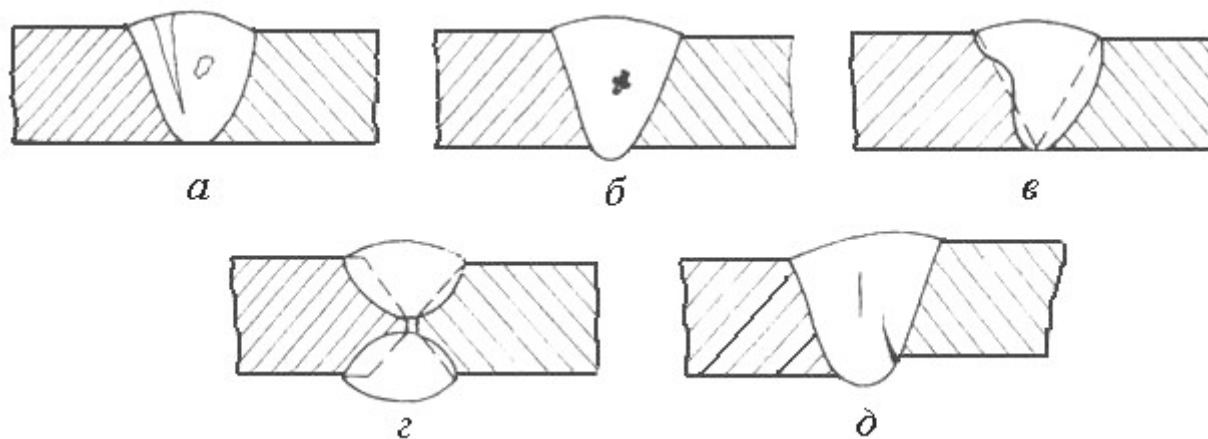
Виды внутренних дефектов сварных соединений: *a* – поры и свищи; *б* – твердые включения (шлак); *в* – несплавление; *г* – непровар; *д* – трещина
